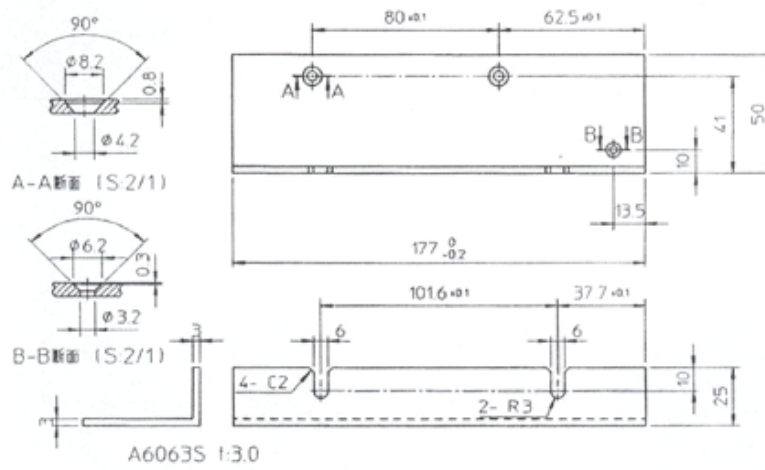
LUG MOUNT 金具 (EIA 规格 左用)
